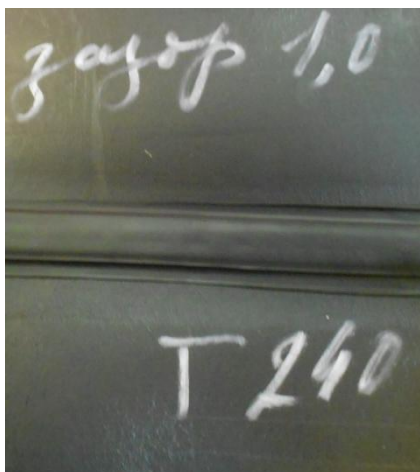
Стыковое сварное соединение С3 толщиной 1,9 мм
